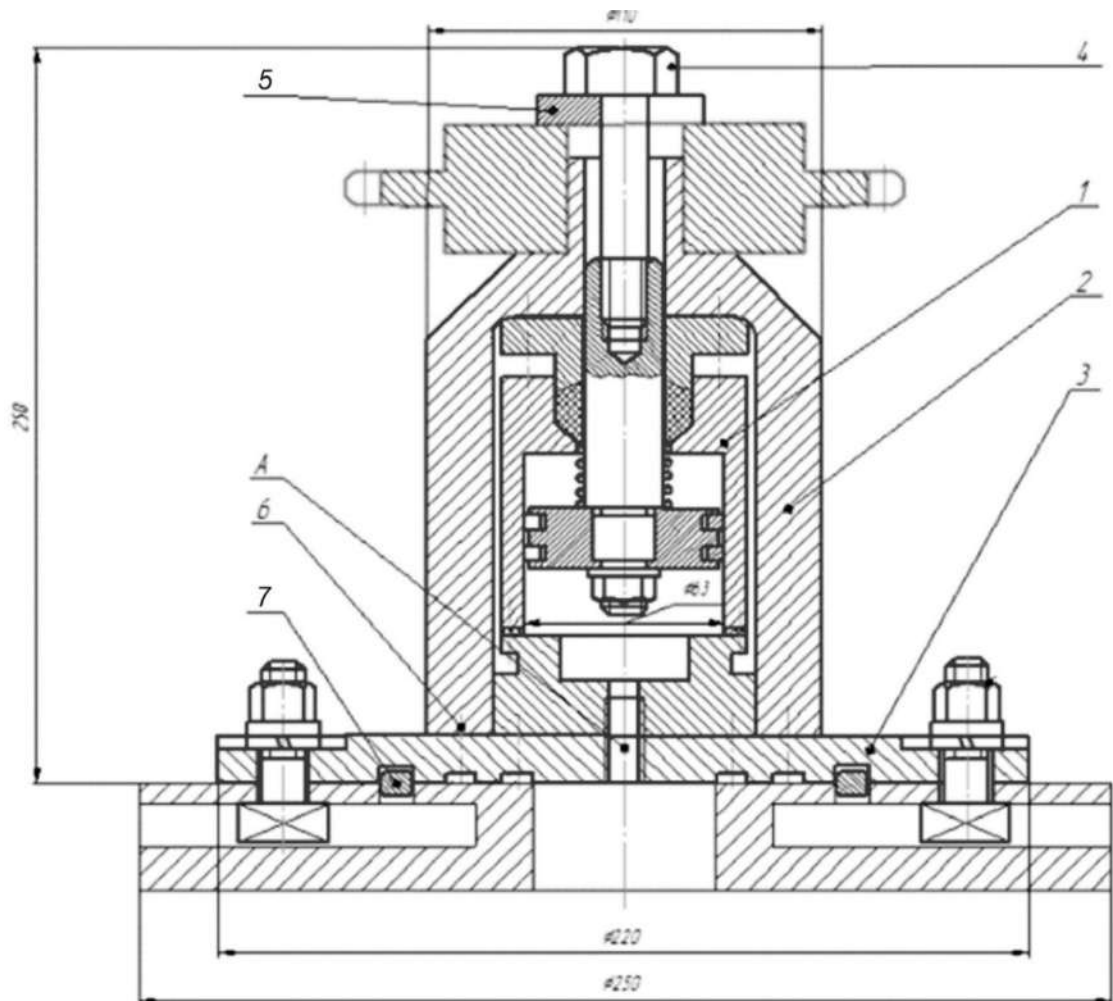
Схема закріплення заготовки в пневматичному пристрої зубофрезерного верстата
